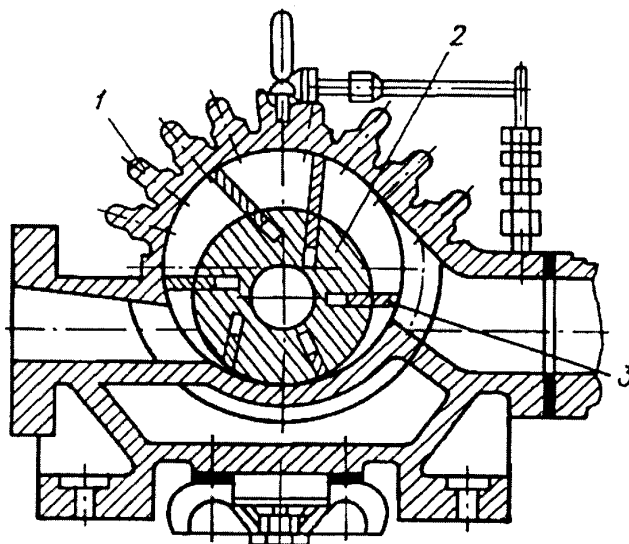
Схема пластинчато-роторной машины: 1 – корпус; 2 – ротор; 3 - пластины
